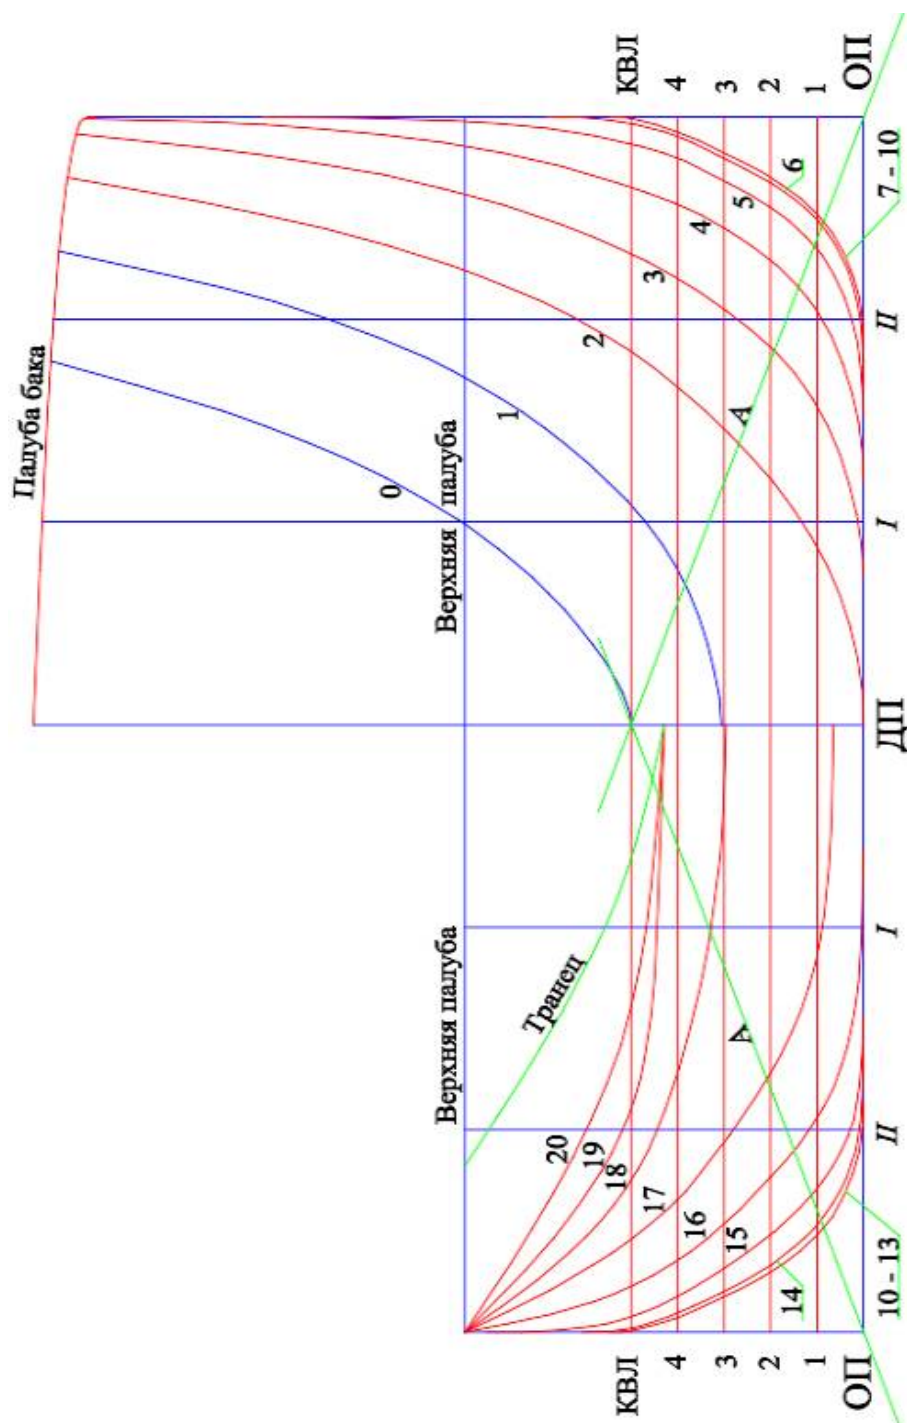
Фрагмент теоретичного креслення корпусу БСДФ ЛК (вид збоку)
